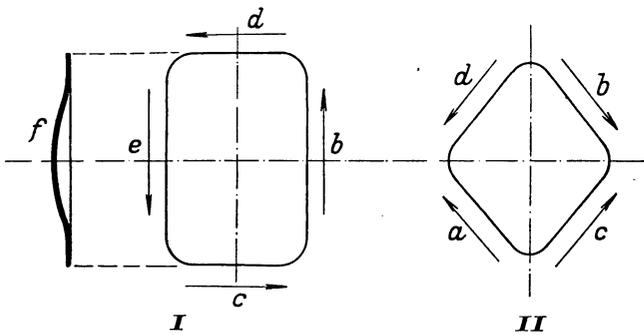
Einschweißen von Flecken bei Dampfkesseln.
